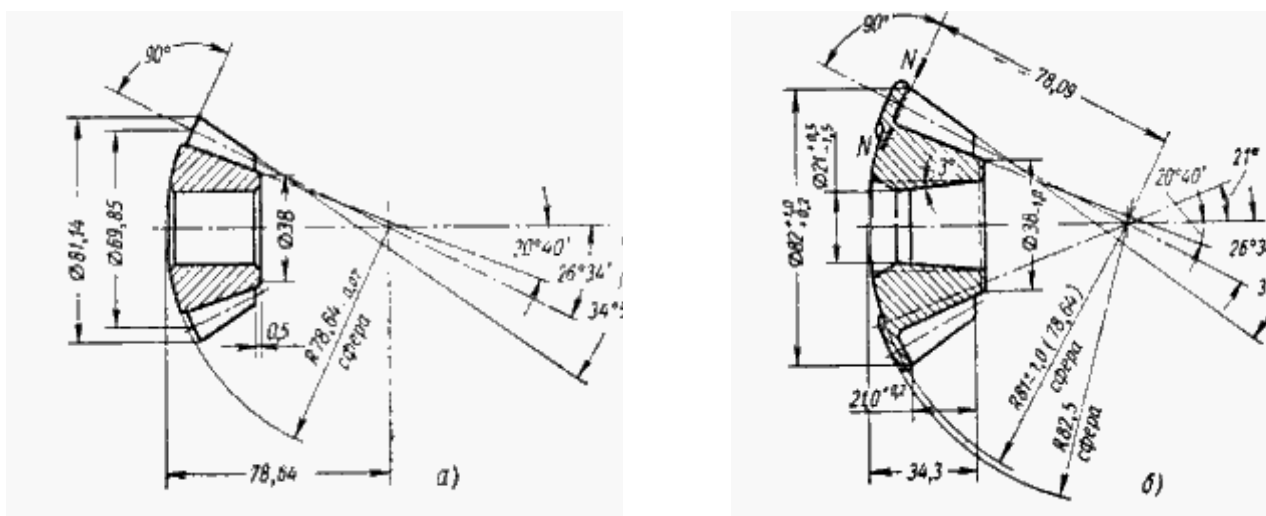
Чертежи детали (а) и поковки (б) сателлита
